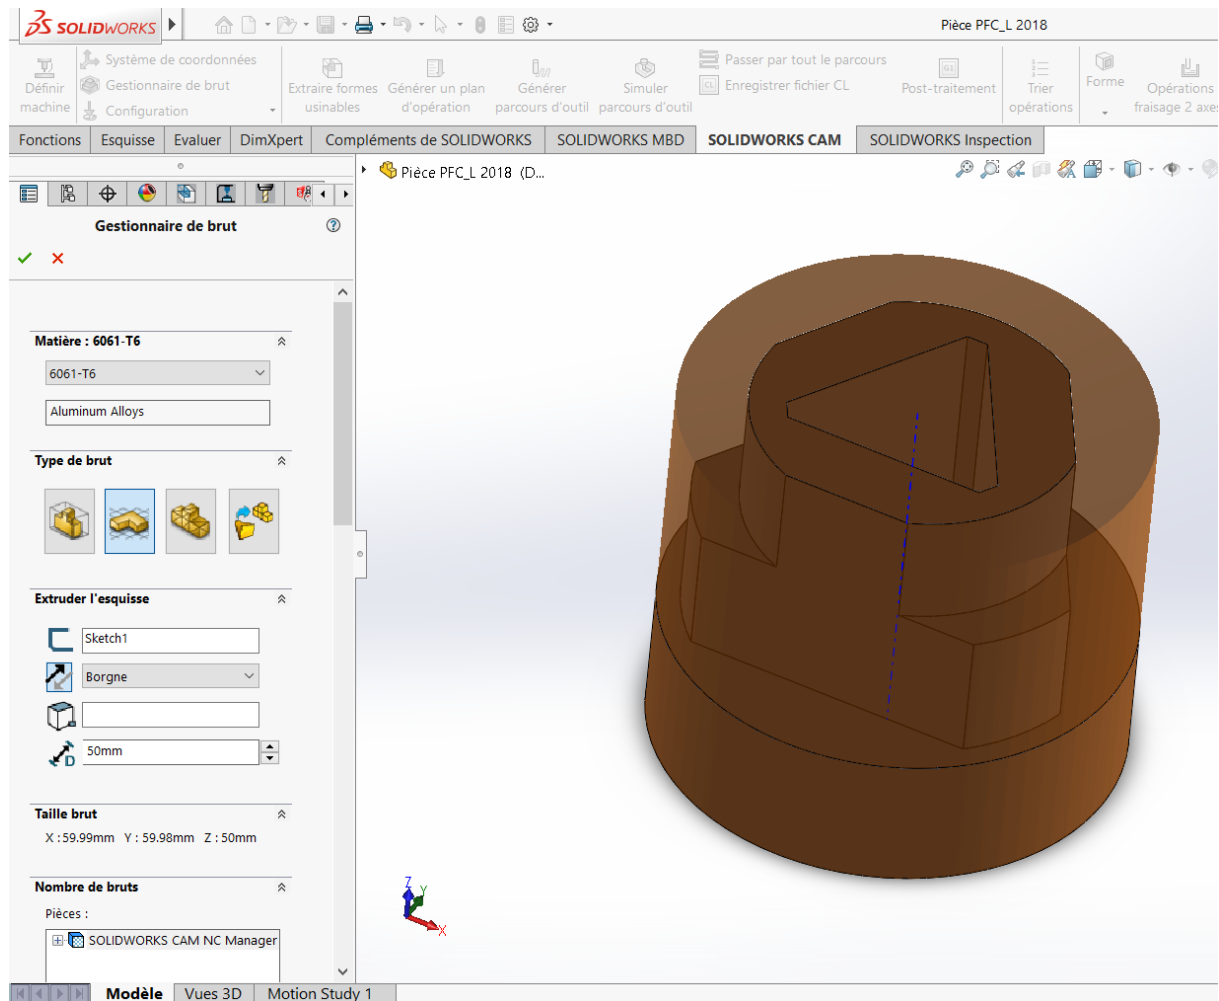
Définition du brut « Stock » sous SolidWorks CAM.
